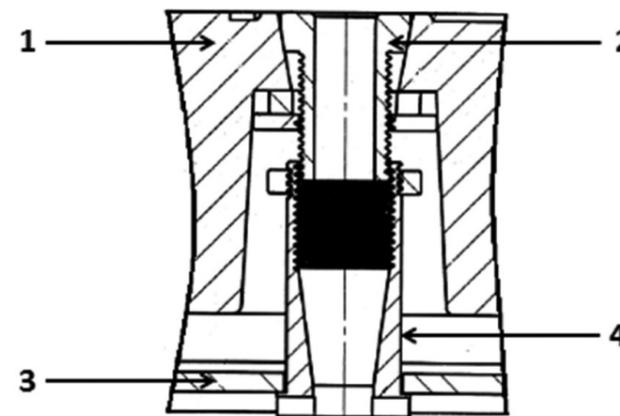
Разрез запорного механизма УЗЛ-Т ССД: 1 – чугунная крышка; 2 – винт, зафиксированный в крышке; 4 – нижняя стальная крышка; 4 – подвижная гайка.
